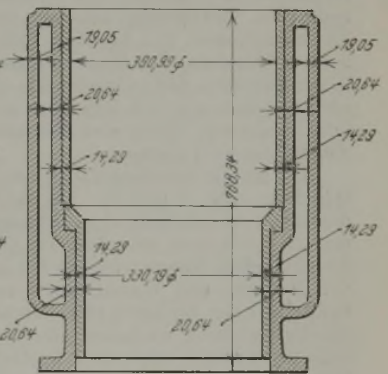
Englischer Kompressorzylinder. Gewicht = 4064 kg.
